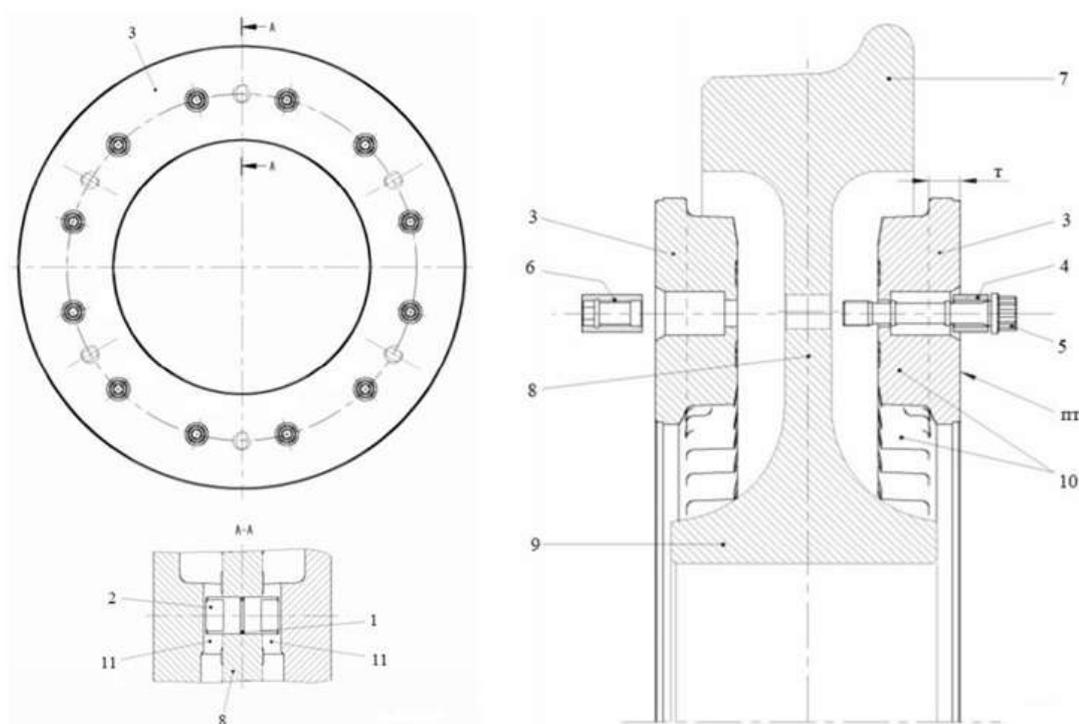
Колесный тормозной диск: 1-уплотнительное кольцо круглого сечения; 2-сухарь; 3-фрикционный диск; 4-компенсационная гильза; 5-винт; 6-втулочная гайка; 7-гребень; 8-диск колеса; 9-втулка колеса; 10-ребро охлаждения; 11-центровочный паз; т-толщина фрикционного ремня; пт-поверхность трения
